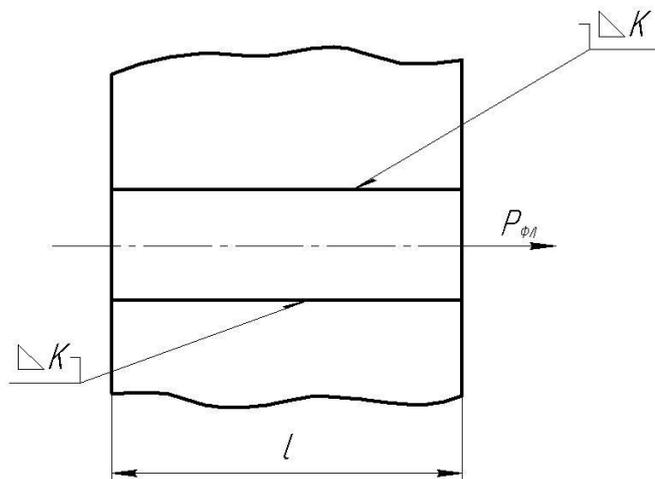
К расчёту сварочного шва.
